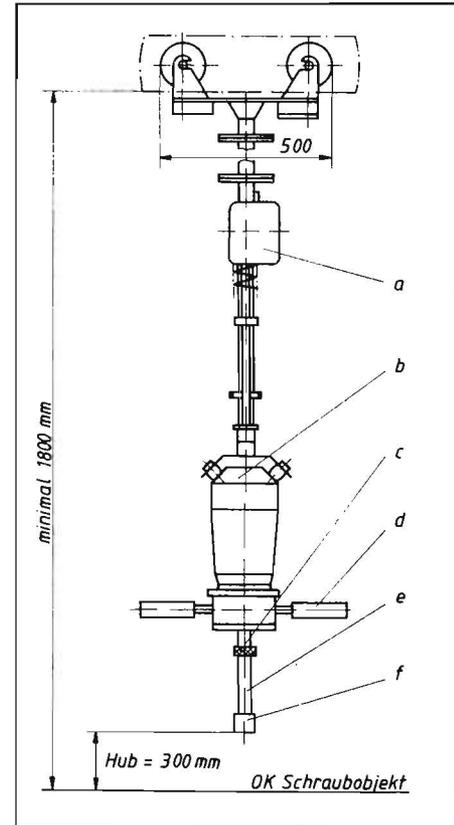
Hydraulischer Einspindelschrauber; a Aufhängung mit Federzug, b Schrauberelement, c Schnellwechsel für Spindel mit Steckfuß, d Haltegriffe mit Druckknopfaster, e Spindel, f Steckfuß entsprechend Schraubobjekt
